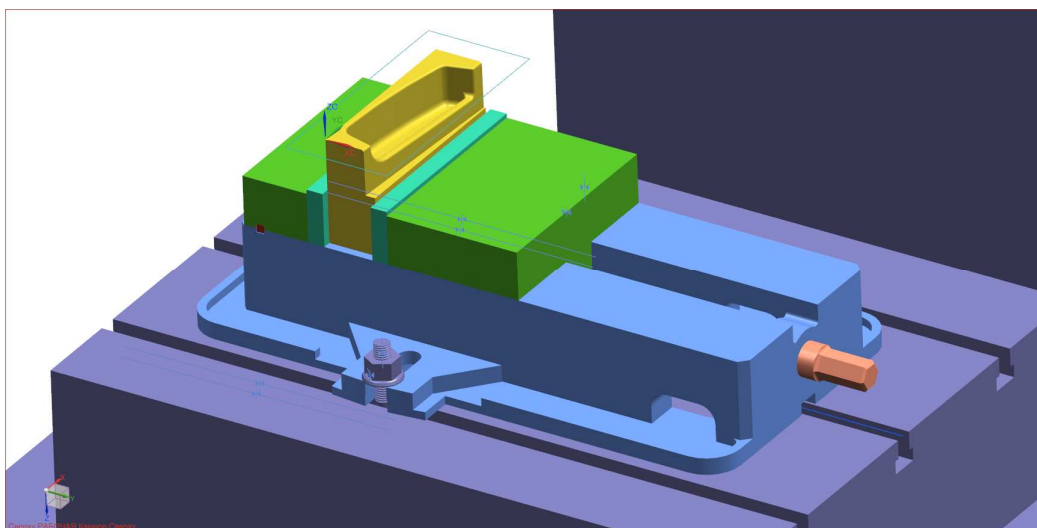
Наладка для чистовой обработки фасонных поверхностей
